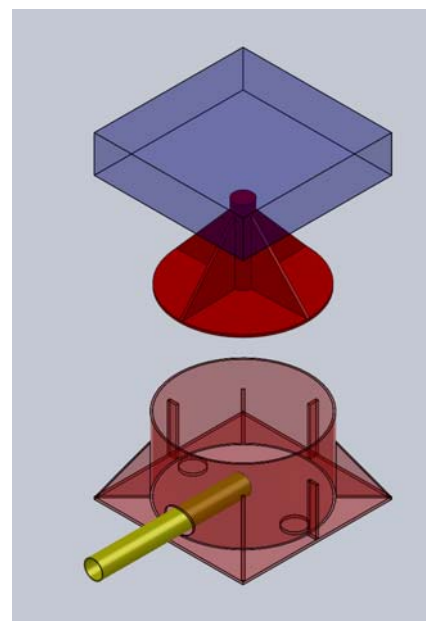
Конструкция испытательного стенда (общий вид)
